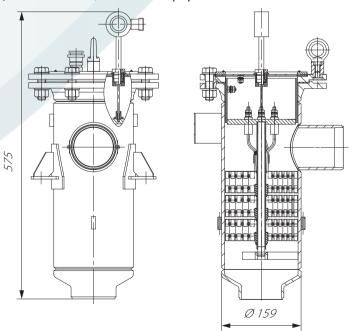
Общий вид электронагревателя РЕ 644.00.00.000.
